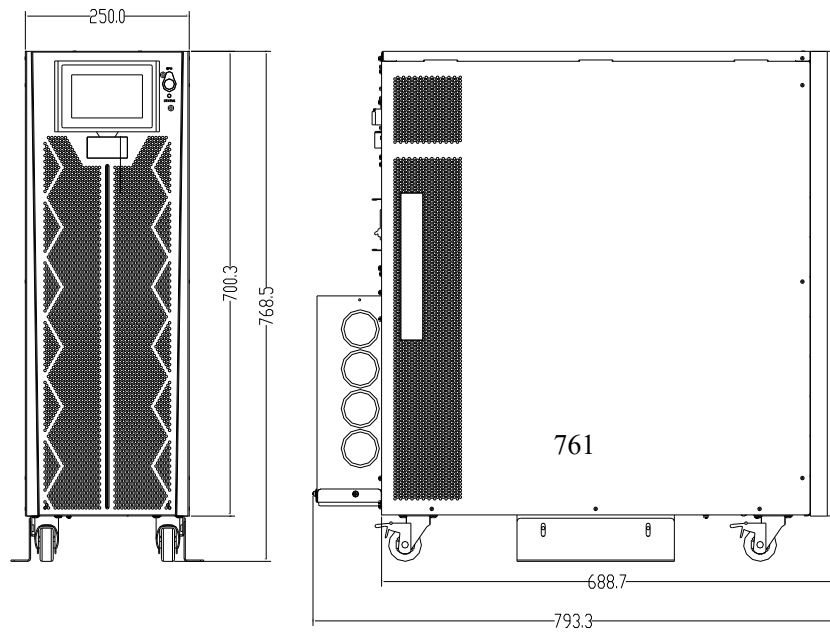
Размеры ИБП 20/30kVA (стандартный типоразмер)
